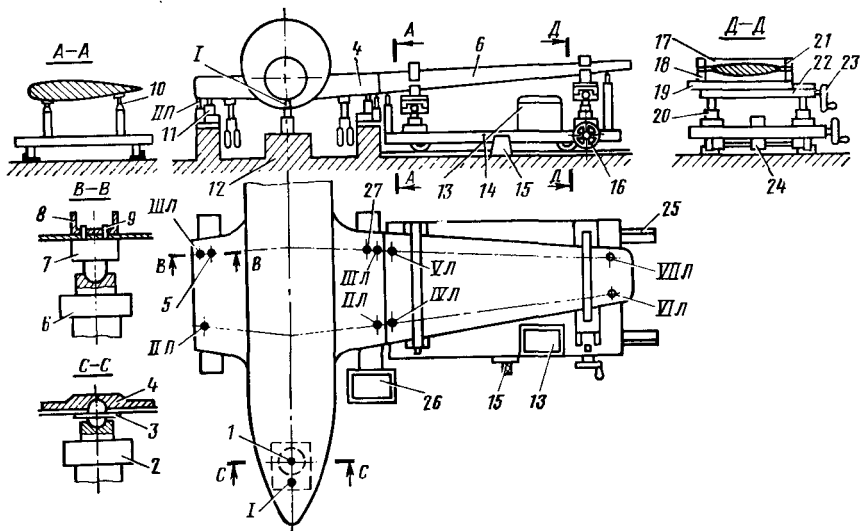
Стенд для стыковки отъемной части крыла (G) с центропланом (V): I, II, III, IV, VII — нивелировочные точки правые (П) и левые (Л); 1, 5, 27 — опорные узлы фюзеляжей и центроплана; 2, 6 — шток гидроподъемника; 3 — шаровая подкладка; 4 — силовой шпангоут; 7 — опора; 8 — задний лонжерон центроплана; 9 — штырь; 10 — пинноль; 11, 2С — гидроподъемник; 12 — фундамент; 13 — насосная станция и пульт управления работой гидроподъемников, установленных на тележке; 14 — тележка; 15 — фиксатор; 16 — штурвал ручного перемещения тележки в продольном направлении; 17 — прижим; 18 — ложемент; 19 — суппорт; 21 — крепление прижима; 22 — каретка суппорта; 23 — рукоятка для перемещения крыла в поперечном направлении; 24 — привод для перемещения каретки в продольном направлении (от электромотора); 25 — рельсовый путь; 26 — насосная станция и пульт управления работой гидроподъемников при установке центроплана в линию полета
